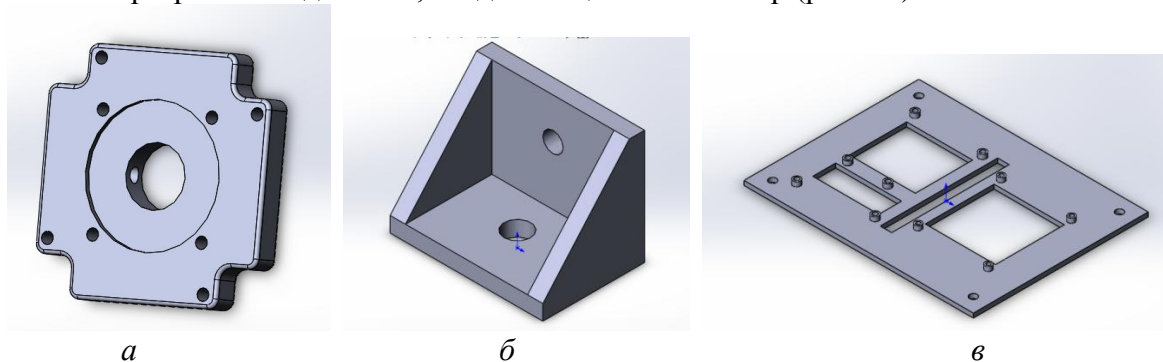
а – вариант крепления для энкодера; б – вариант крепления для драйвера; в – плата
